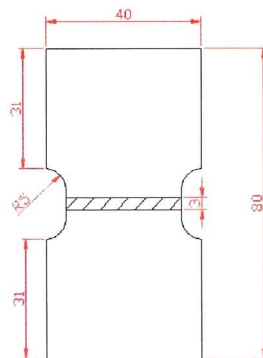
Eprouvette pour la machine bi-axiale (mm).
